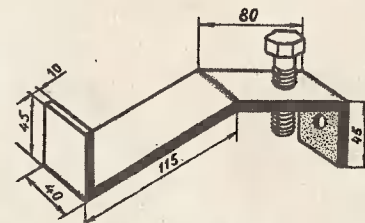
Приспособление для выпрессовки шкворневого пальца: 1 — амортизатор; 2 — шкворневой палец.
